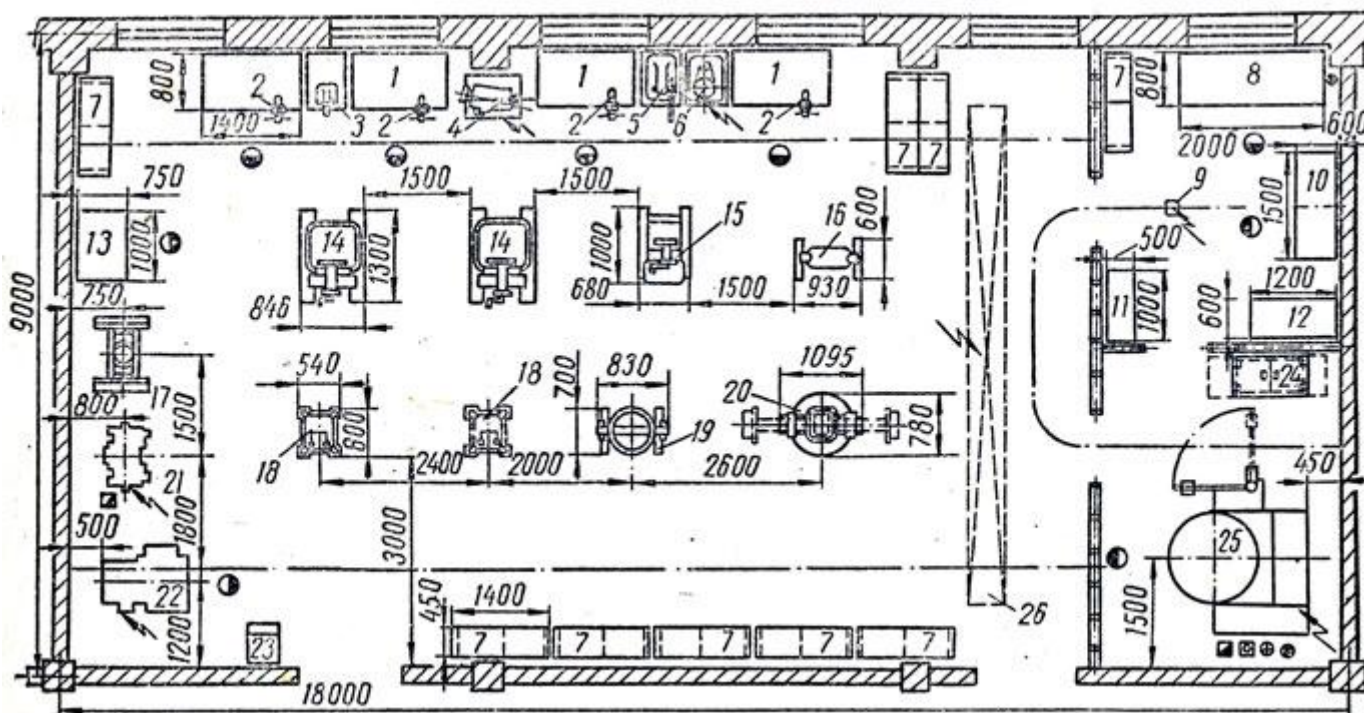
Планировка агрегатного цеха: 1 - слесарные верстаки; 2 - слесарные тиски; 3 - прибор для проверки поршня с шатуном; 4 - станок для шлифовки клапанов; 5 - пресс с ручным приводом; 6 - настольный сверлильный станок; 7 - стеллажи; 8 - стол для контроля и сортировки деталей; 9 - тельфер; 10 - унивеосальные центры для проверки валов; 11 - ларь для обтирочных материалов; 12 - шкаф для приборов; 13 - поверочная плита; 14 и 15 - стенды для ремонта двигателей; 16 - стенд для ремонта рулевых механизмов и карданных валов; 17 - гидравлический пресс; 18 - стенд для ремонта коробок передач; 19 - стенд для ремонта редукторов задних мостов; 20 - стенд для ремонта передних и задних мостов; 21 - станок для заточки инструментов; 22 - вертикально-сверлильный станок; 23 - инструментальный шкаф; 24 - ванна для мойки мелких деталей; 25 - установка для механизированной мойки крупных деталей; 26 - подвесная кран-балка
